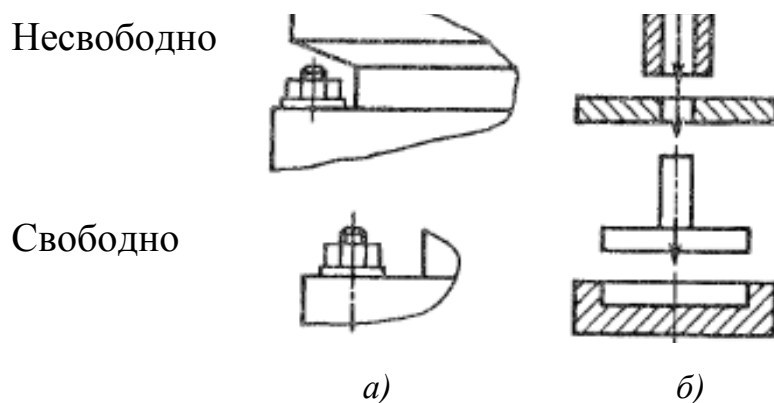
Примеры конструкций с несвободным и свободным доступом (а) сборочного инструмента к гайке и одним вертикальным (сверху вниз) (б) направлением сборки
